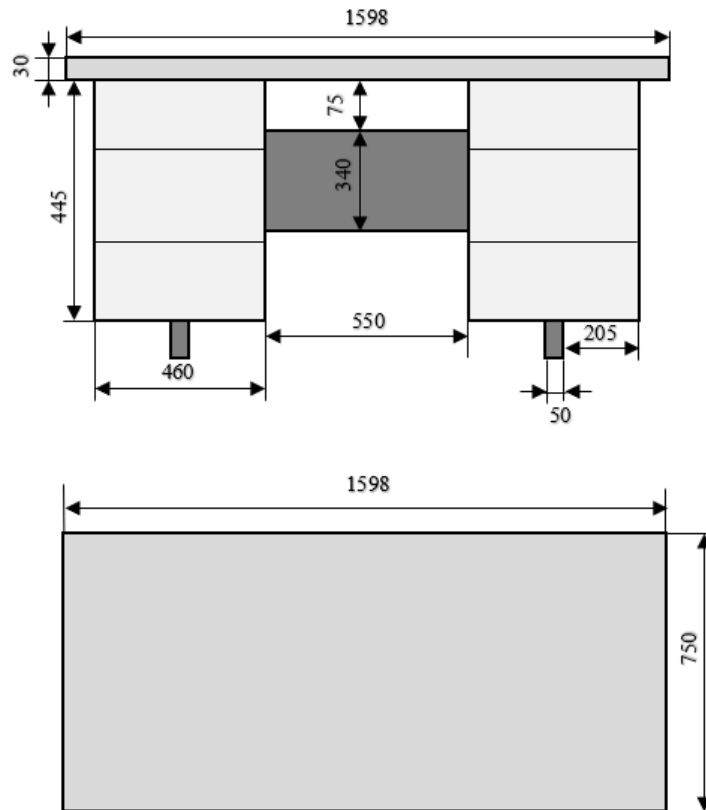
Croquis puesto de trabajo trabajadora 4. Fuente: elaboración propia
